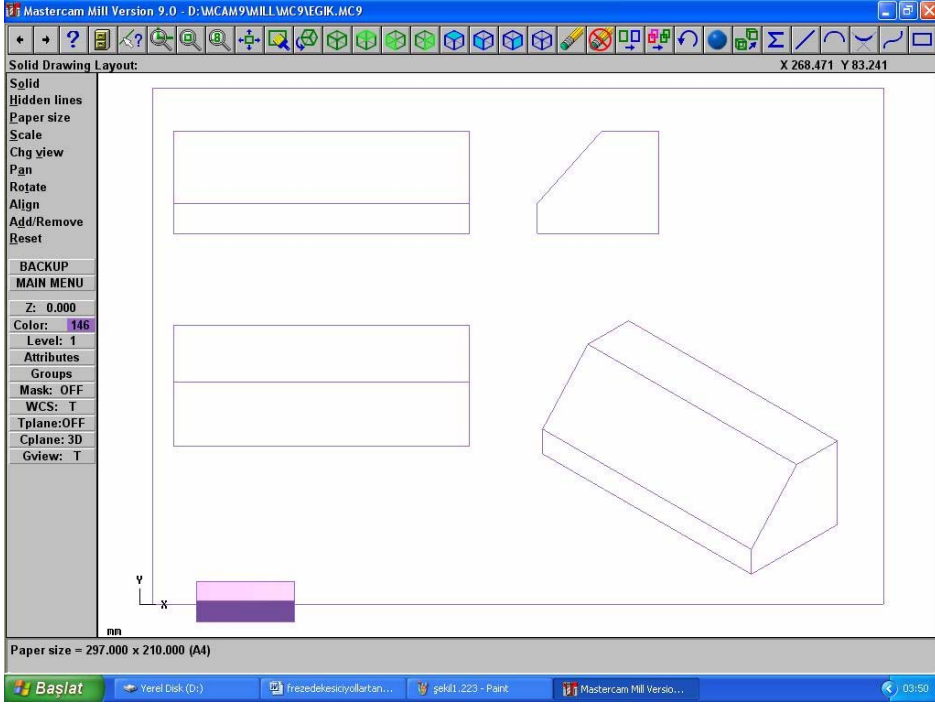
Layout (Görünüş planı) diyalog kutusu
